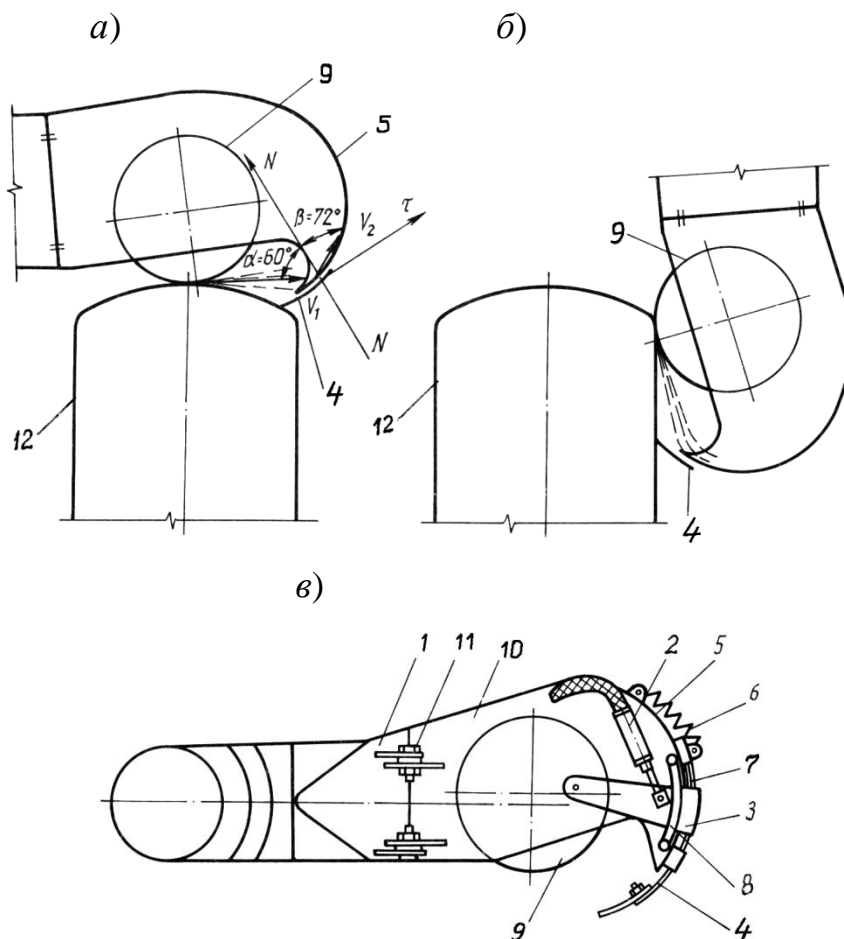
Устройство отсоса пылеприёмника шероховального станка:
